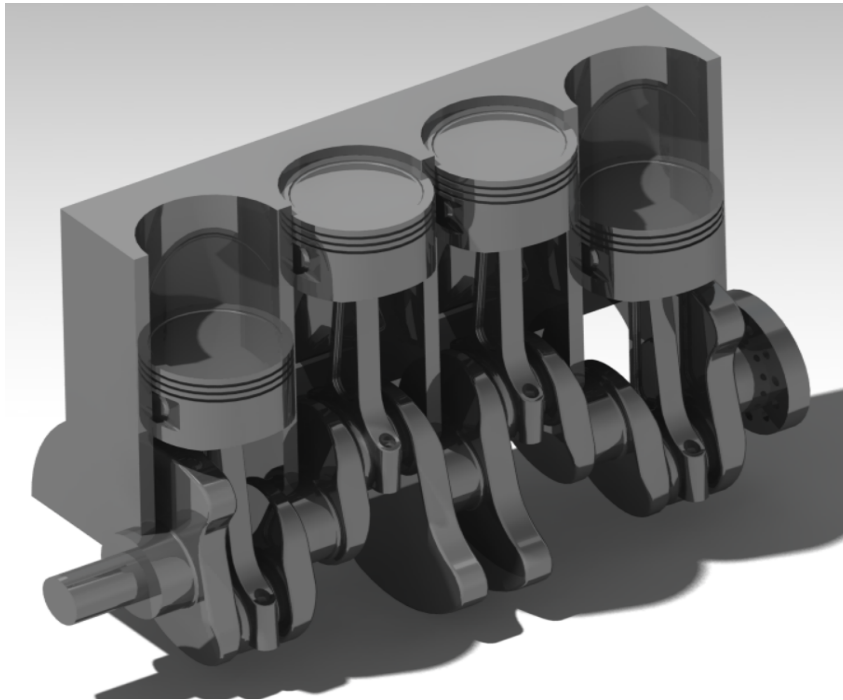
Vue de l'assemblage final du moteur.
